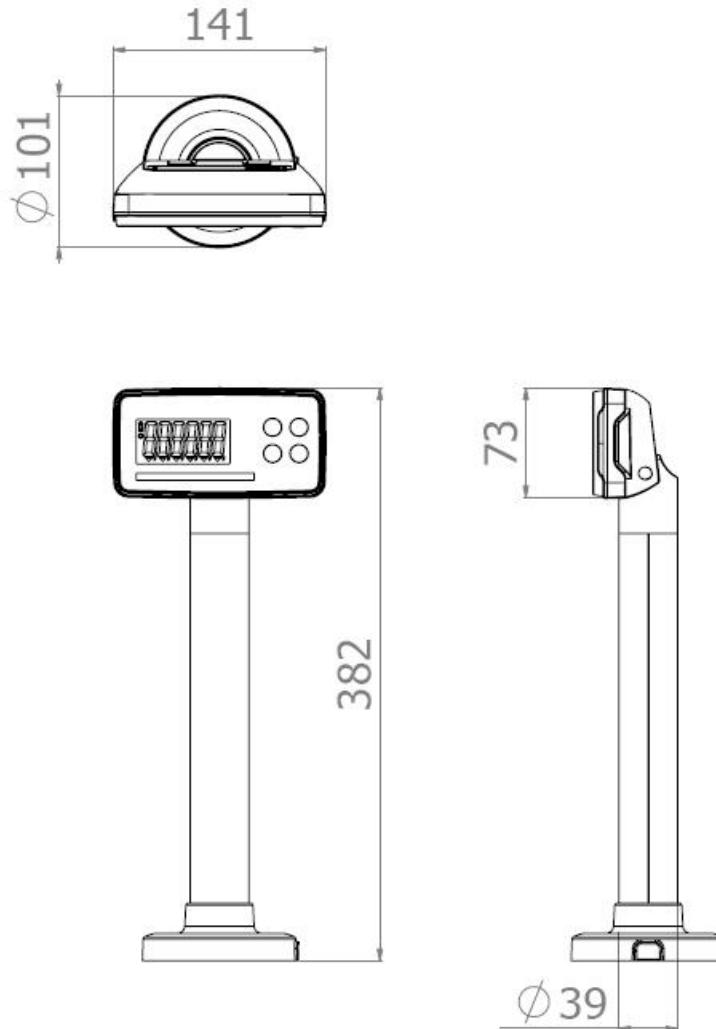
Габаритные размеры индикаторной головки в сборе со стойкой
